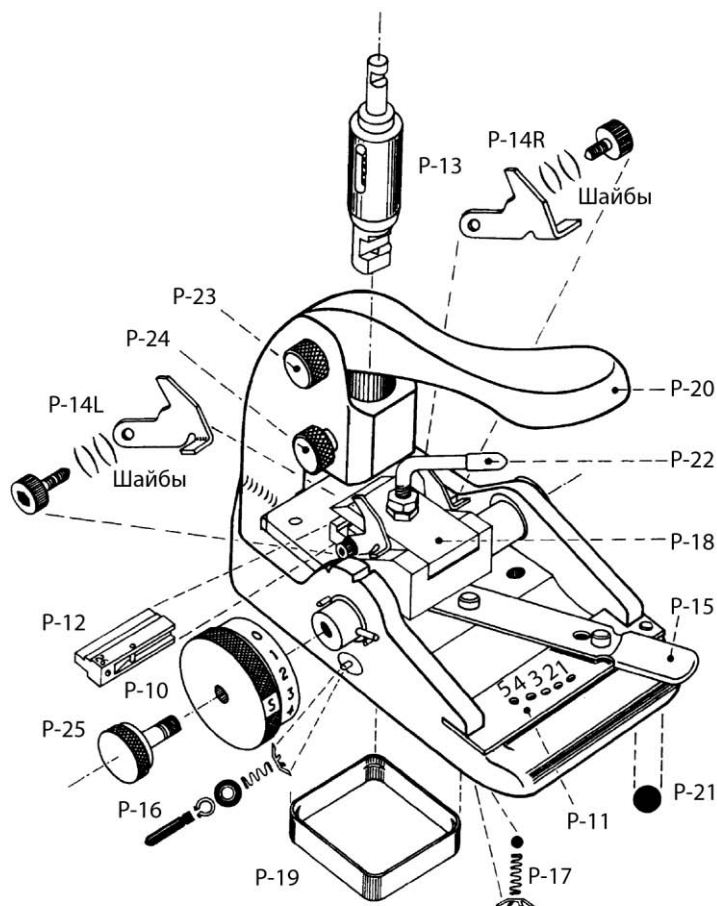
Детали станка для изготовления ключей Ехаста: P-10 — переключатель глубины (для различных ключей обозначается разными буквами А, В и т. п.); P-17 — фиксатор пластины для разметки позиций; P-18 — блок каретки; P-11 — пластина для разметки позиций (для ключей различных производителей обозначаются разными номерами 100, 101 и т. п.); P-19 — пластмассовый короб; P-12 — вставка для ключа (для ключей различных производителей отличаются по номерам 1, 2 и т. п.); P-20 — рычаг; P-21 — фетровые подкладки (4 шт.); P-13 — блок пуансона и матрицы; P-22 — рычаг каретки; P-14R — блок направляющей запящичка (правая сторона); P-23 — винт фиксации рычага; P-14L — блок направляющей запящичка (левая сторона); P-24 — крепежный винт матрицы; P-15 — блок рычага выставления позиций; P-25 — винт фиксации переключателя глубины; P-16 — фиксатор переключателя глубины (С разрешения компании Ilco Unican Corp.)
